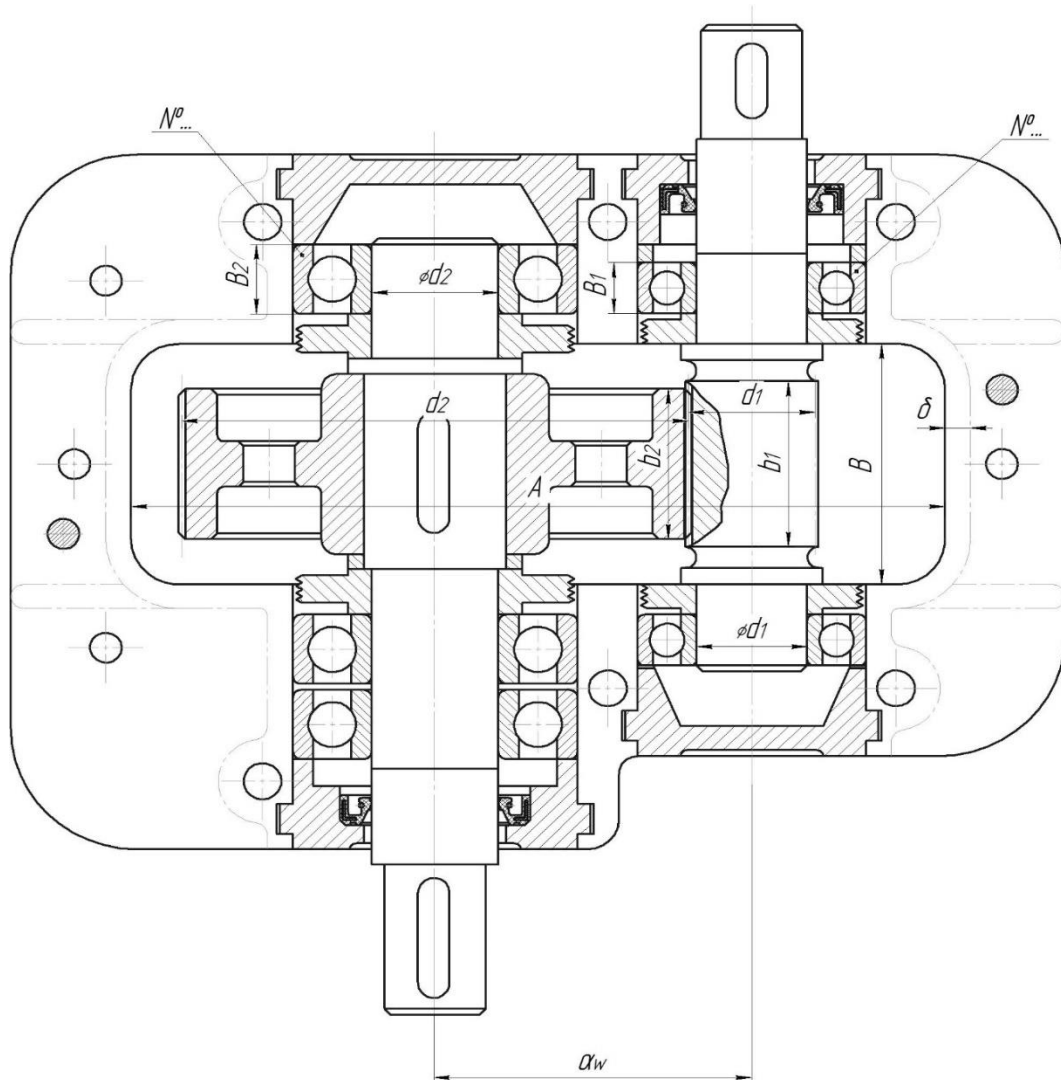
Компонівка циліндричного одноступеневого прямозубого редуктора
